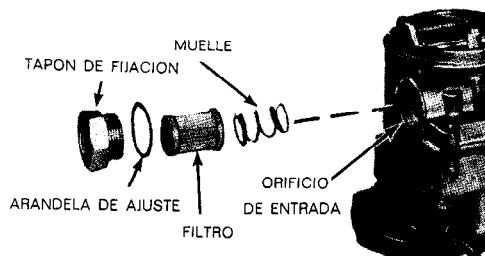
Filtro de combustible instalado en el carburador (Buick Motor Division of General Motors Corporation).
